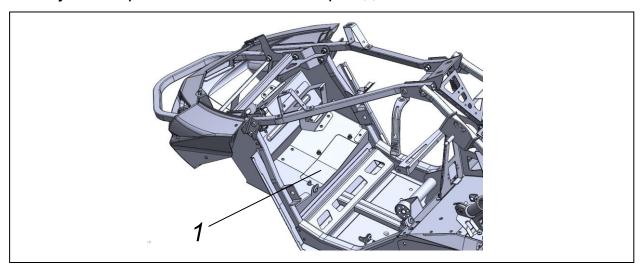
Расположение лючка для слива моторного масла 1 – лючок для слива моторного масла.
